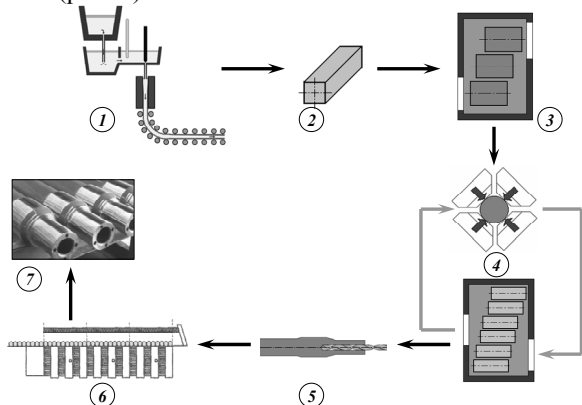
Вариант технологии изготовления полрой оси из сплошной непрерывнолитой заготовки квадратного сечения (многократная ковка)
